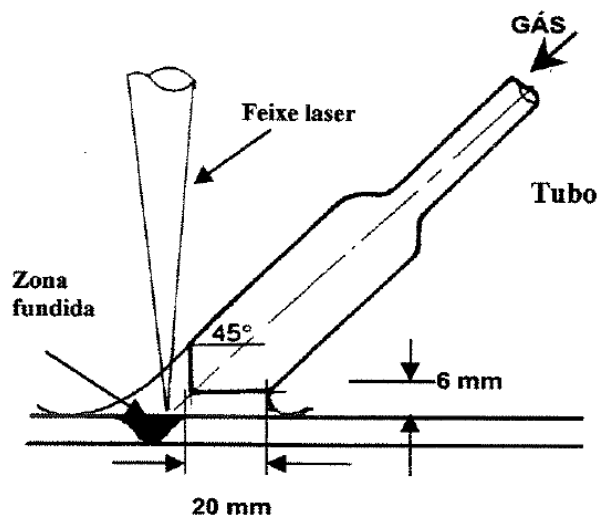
Posicionamento do bico de gás de proteção ideal para a realização da soldadura ([Pastor 1999](#))
